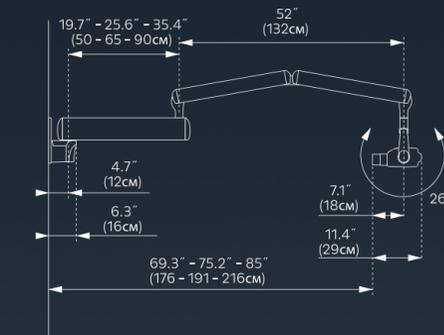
Представлены размеры для одинарного крепления и короткого конуса. Крепление с двумя шпильками дополнительно удлиняет конструкцию на 3,0 см.
